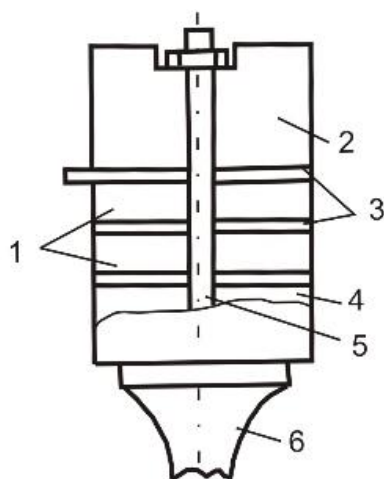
Пакетный пьезокерамический преобразователь с пассивными накладками:
